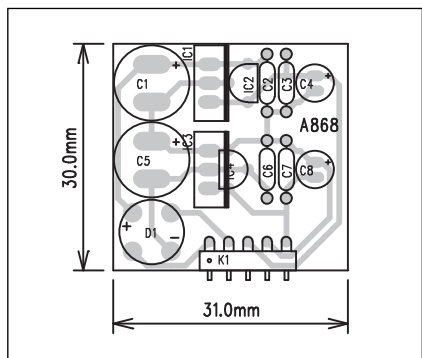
Obrazec desky spojů modulu (A99867)
